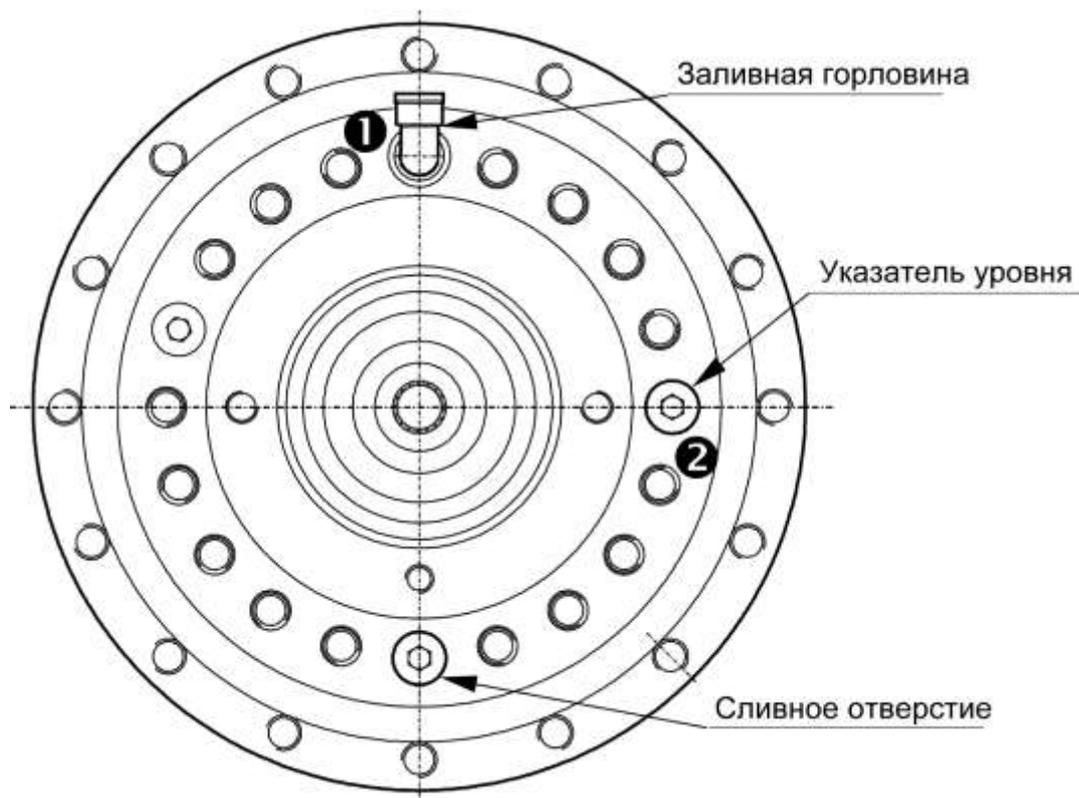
Схема залива и слива масла из редуктора лебедки и контроля уровня
